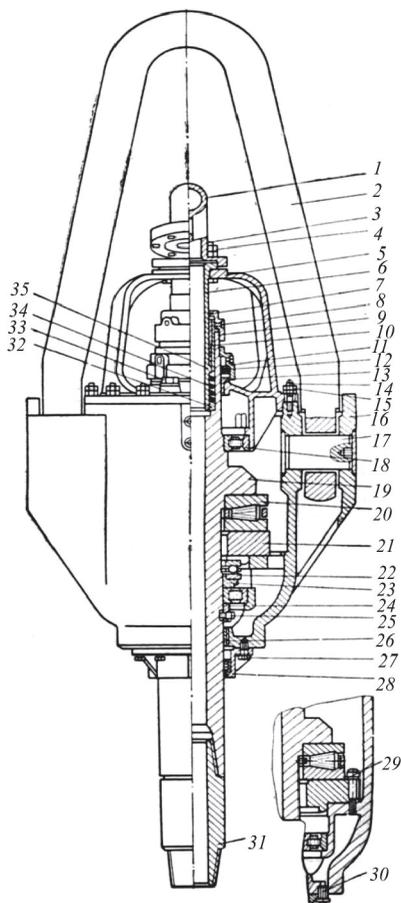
Вертлюг: 1 – подвод; 2 – штроп; 3 – болты; 4 – гайка; 5 – крышка; 6 – грязевая труба; 7 – нажимная гайка; 8 – масленка грязевого сальника; 9 – втулка грязевого сальника; 10 – самоуплотняющиеся манжеты грязевого сальника; 11 – корпус масляного сальника; 12 – самоуплотняющиеся манжеты масляного сальника; 13 – втулка масляного сальника; 14, 15 – шпильки; 16 – корпус; 17 – палец; 18 – роликовый подшипник; 19 – ствол; 20 – основная опора; 21 – плита опоры; 22 – шариковый упорный подшипник; 23 – опора шарикового подшипника; 24 – установочная гайка; 25 – установочные винты; 26 – втулка; 27 – болты; 28 – сальник; 29 – специальные винты; 30 – пробка для слива масла; 31 – переводник; 32 – грундбукса грязевого сальника; 33 – пробка для залива масла; 34 – пружина грязевого сальника; 35 – поджимное кольцо
